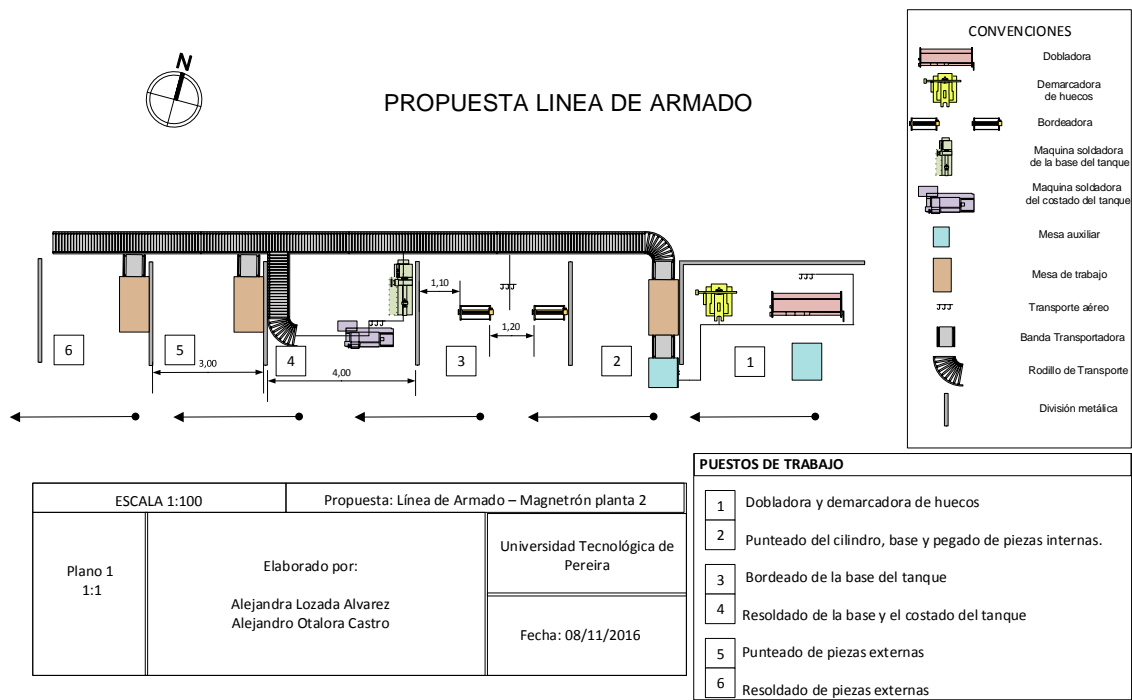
Propuesta distribución de la línea de armado. [Anexo B](#)
